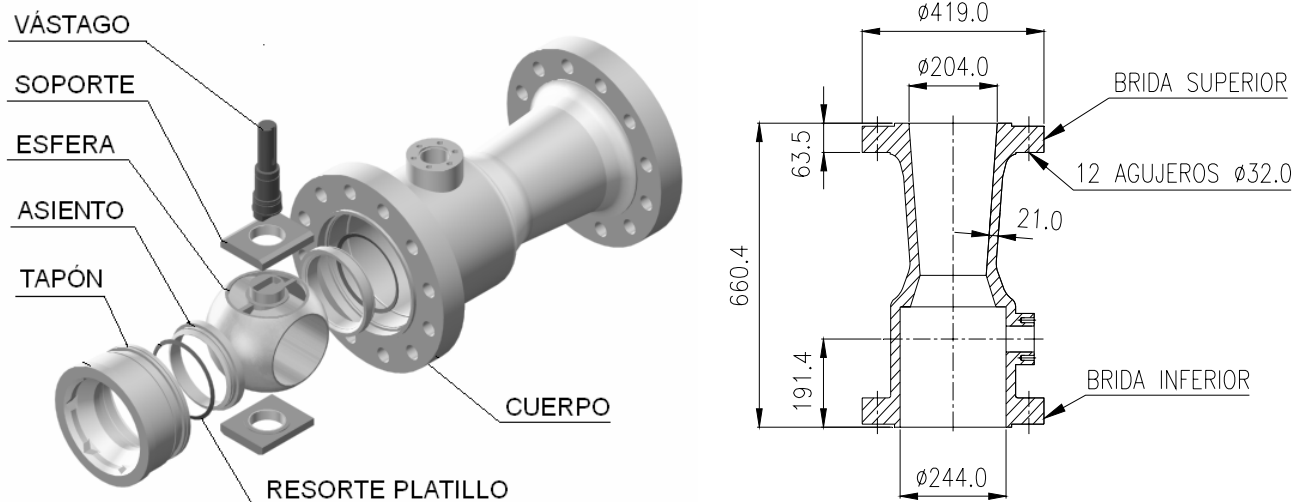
Válvula del tipo esférica - Principales componentes y dimensiones generales del cuerpo.
